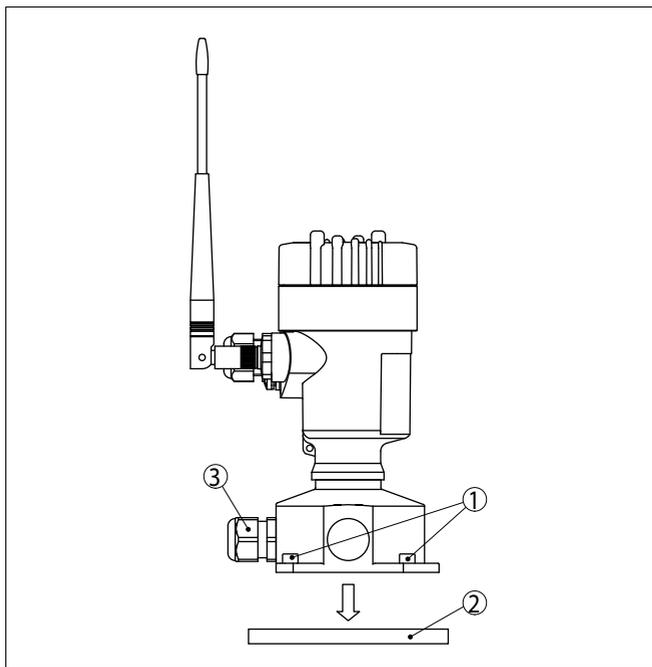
Снятие монтажной пластины с цоколя корпуса
